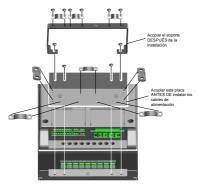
Acoplamiento de la placa PE y del soporte de cables API, MI4 - MI5
